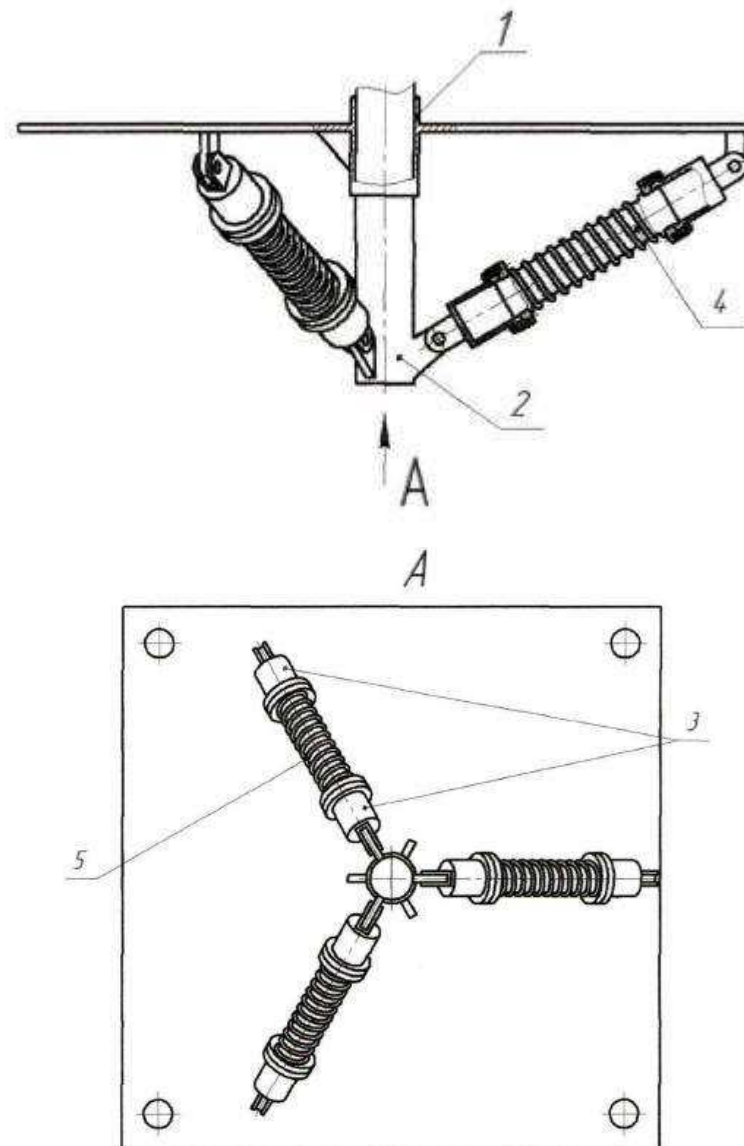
Пружинний віброізолятор [7]: 1 – корпус, 2 – стійка, 3 – стакан, 4 – повзунки, 5 – пружини
